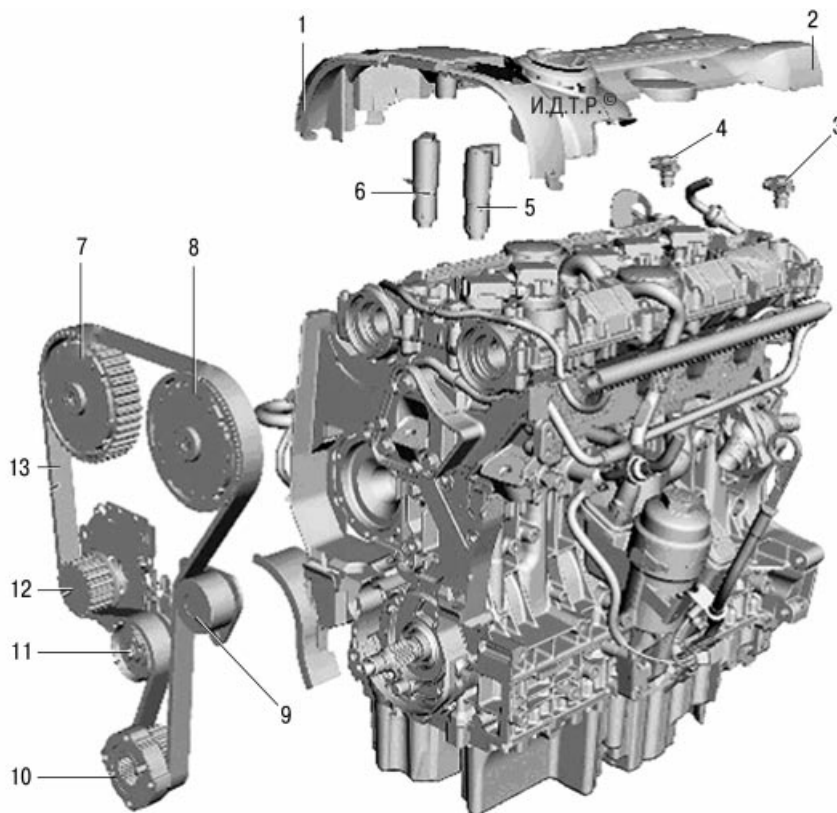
Двигатель Duratec-V15 объемом 2,5 л с элементами системы изменения фаз газораспределения: 1 – крышка привода газораспределительного механизма; 2 – крышка головки блока цилиндров; 3 – датчик положения впускного распределительного вала; 4 – датчик положения выпускного распределительного вала; 5 – электромагнитный клапан регулировки положения впускного распределительного вала; 6 – электромагнитный клапан регулировки положения выпускного распределительного вала; 7 – механизм регулировки положения выпускного распределительного вала; 8 – механизм регулировки положения впускного распределительного вала; 9 – промежуточный шкив ремня привода газораспределительного механизма; 10 – зубчатый шкив ремня привода газораспределительного механизма на коленчатом валу; 11 – натяжитель ремня привода газораспределительного механизма; 12 – зубчатый шкив насоса охлаждающей жидкости; 13 – ремень привода газораспределительного механизма
